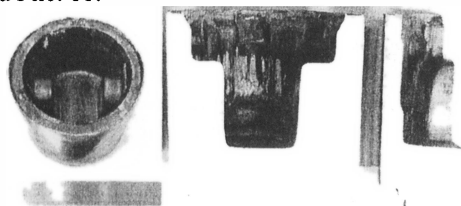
Общий вид и разрезы тиксопрессованных заготовок поршней ДРЦ-85 из сплава АЛ25
